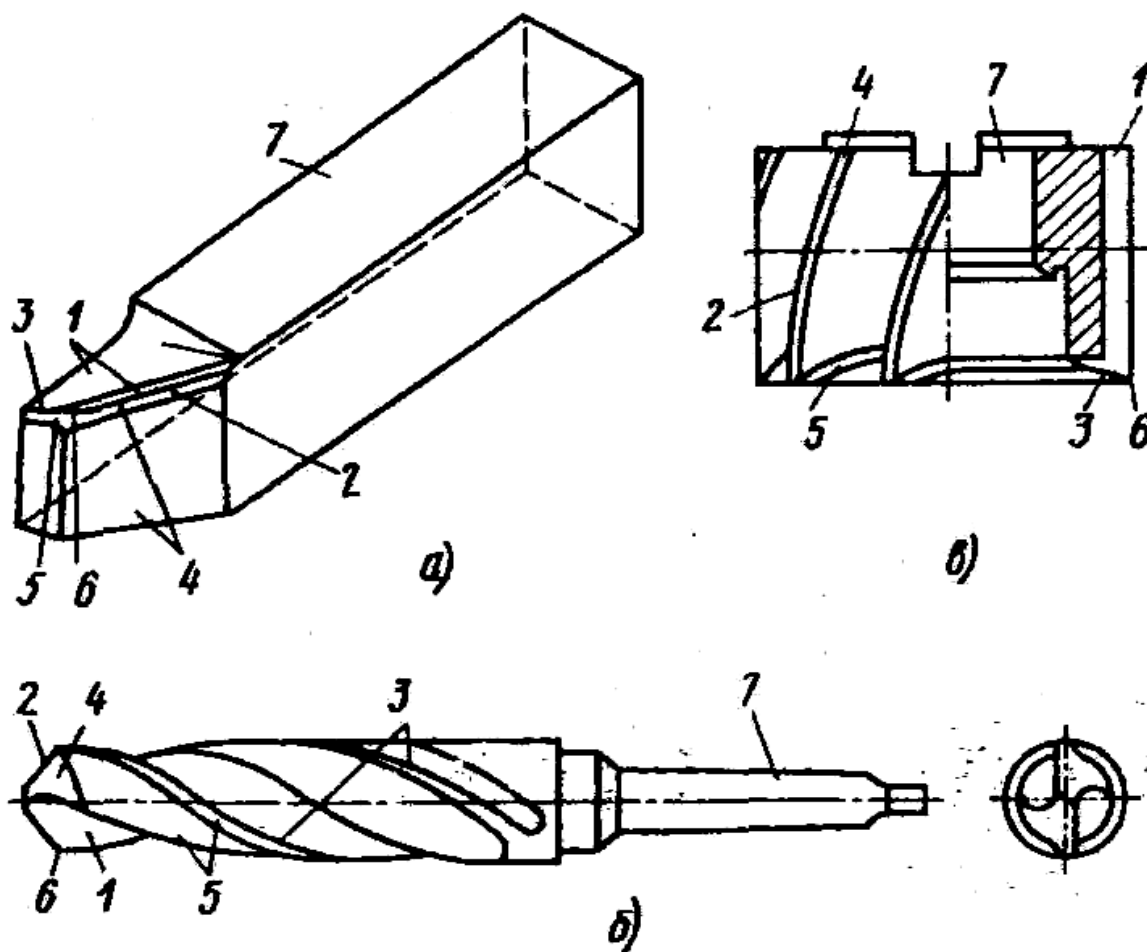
Геометрические и конструктивные элементы режущих инструментов: а – токарного резца; б – сверла; в – фрезы:
